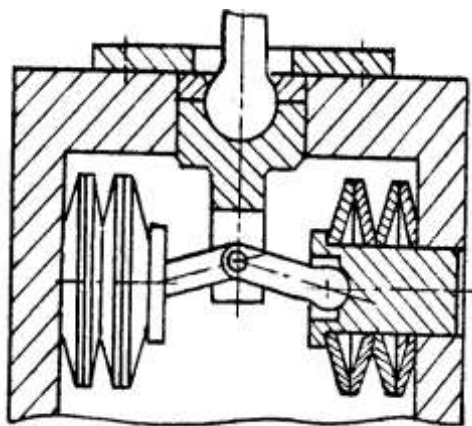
Неразрушающийся пружинно-рычажный предохранитель
